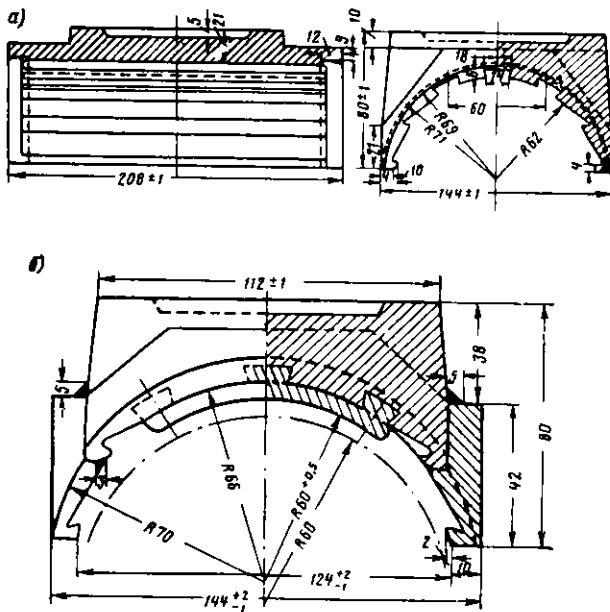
Корпуса подшипников с увеличенным углом обхвата
